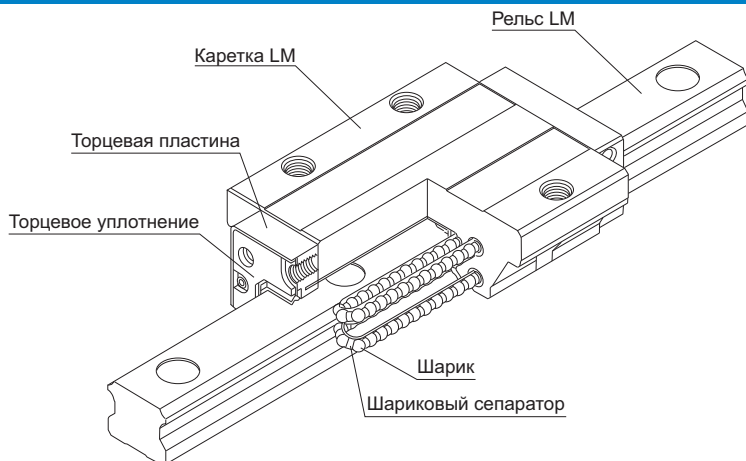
Чертеж конструкции шариковой рельсовой направляющей LM с сепаратором модели SHS
